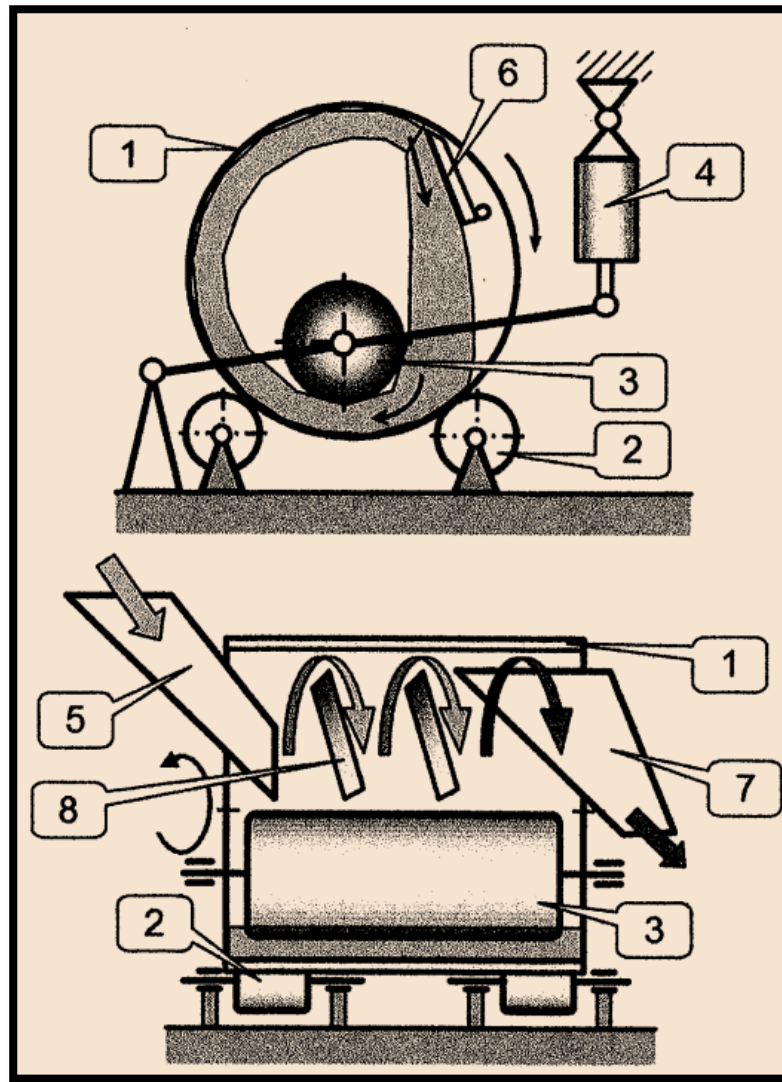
Схема барабанно-валкового активатора безперервної дії: 1 – барабан; 2 – ролики; 3 – валок; 4 – пристрій для притискання валка до внутрішньої поверхні барабана; 5 – завантажувальний лоток; 6 – ніж; 7 – розвантажувальний лоток; 8 – напрямний елемент для регулювання осьового переміщення матеріалу.
